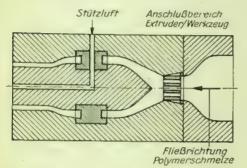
Extrusionswerkzeug für Hohlprofile
